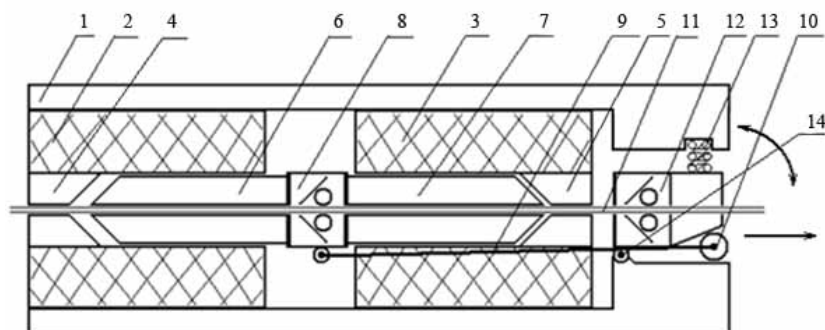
Конструкция импульсного механизма подачи сварочной проволоки.
